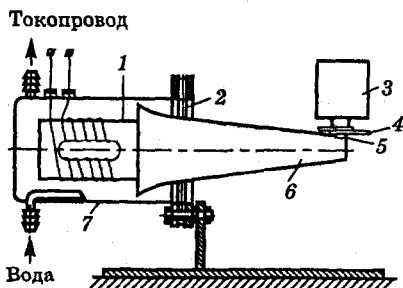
Схема установки для точечной сварки ультразвуком
